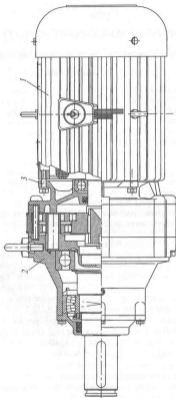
Планетарно-цепочный одноступенчатый мотор-редуктор
